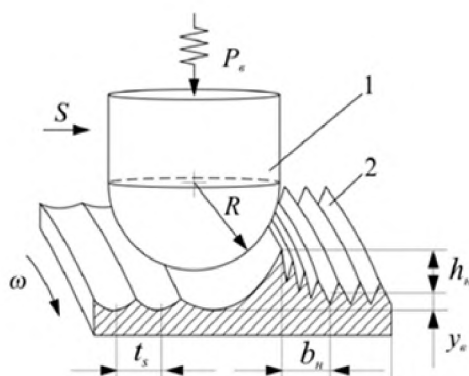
Схема при алмазном выглаживании поверхности детали: 1 – алмаз; 2 – обрабатываемая поверхность; R – радиус алмаза; ts – шаг подачи; ω – угловая скорость детали [2].
